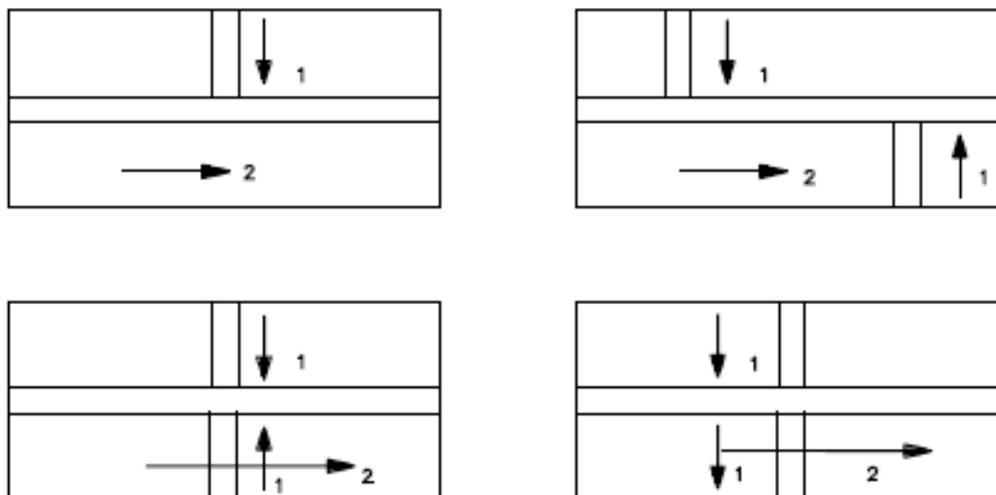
Uniones planas con soldaduras cruzadas.
